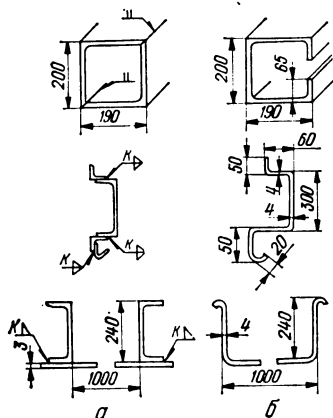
Примеры замены сварных конструкций (а) готовыми гнутыми профилями (б).
